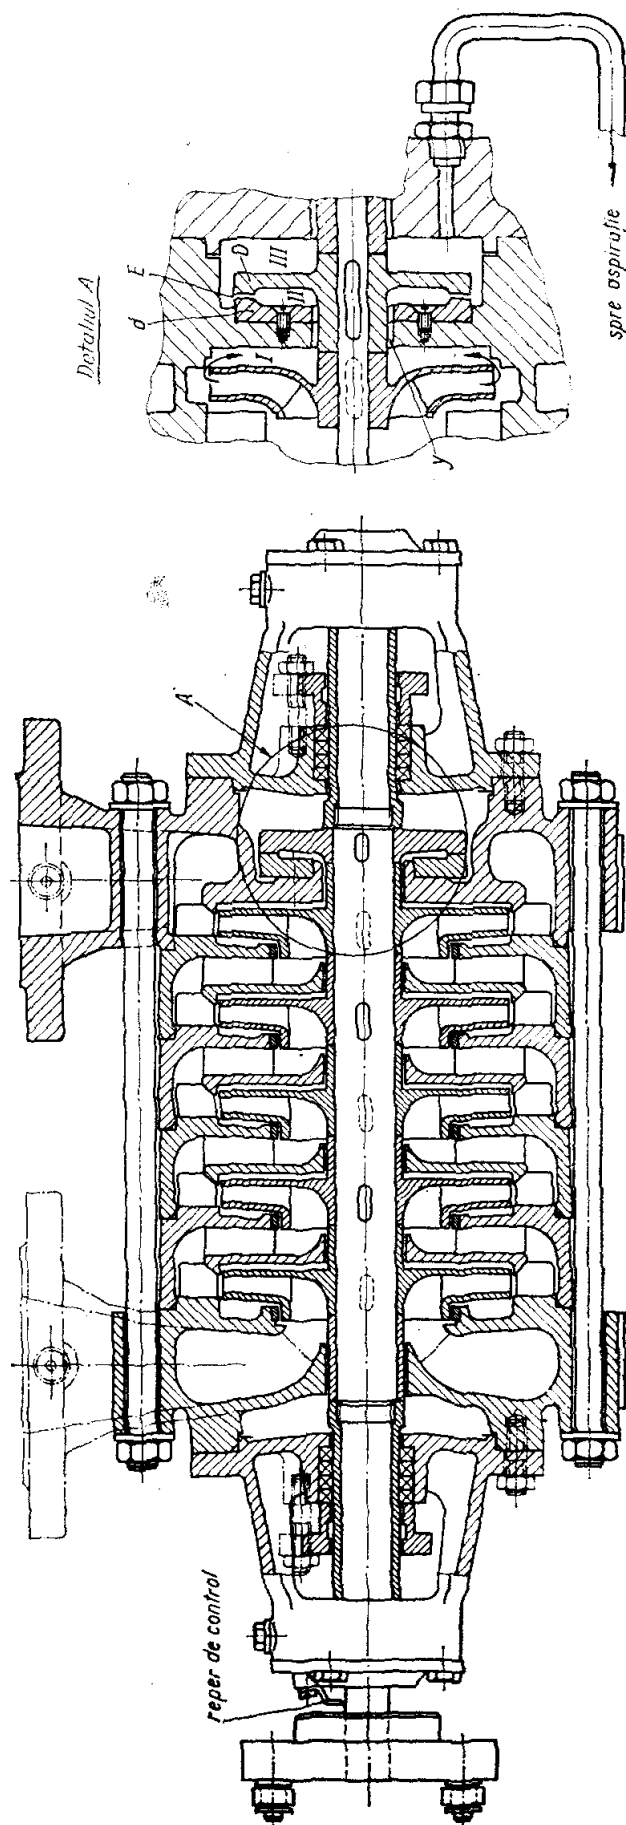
Pompă multietajată cu disc de echilibrare.
